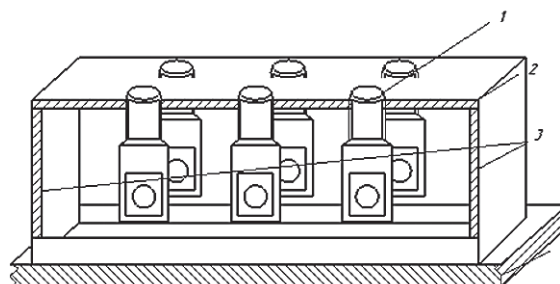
Шестистоечное приспособление для шлифования торца корпуса форсунки:
